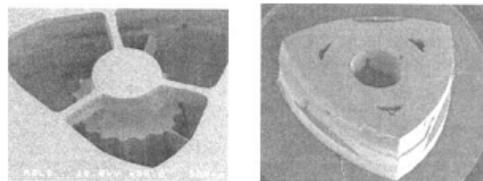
CWRU микро-роторный двигатель. Слева: трёхпластинчатая Si форма; справа: формованный SiC ротор
